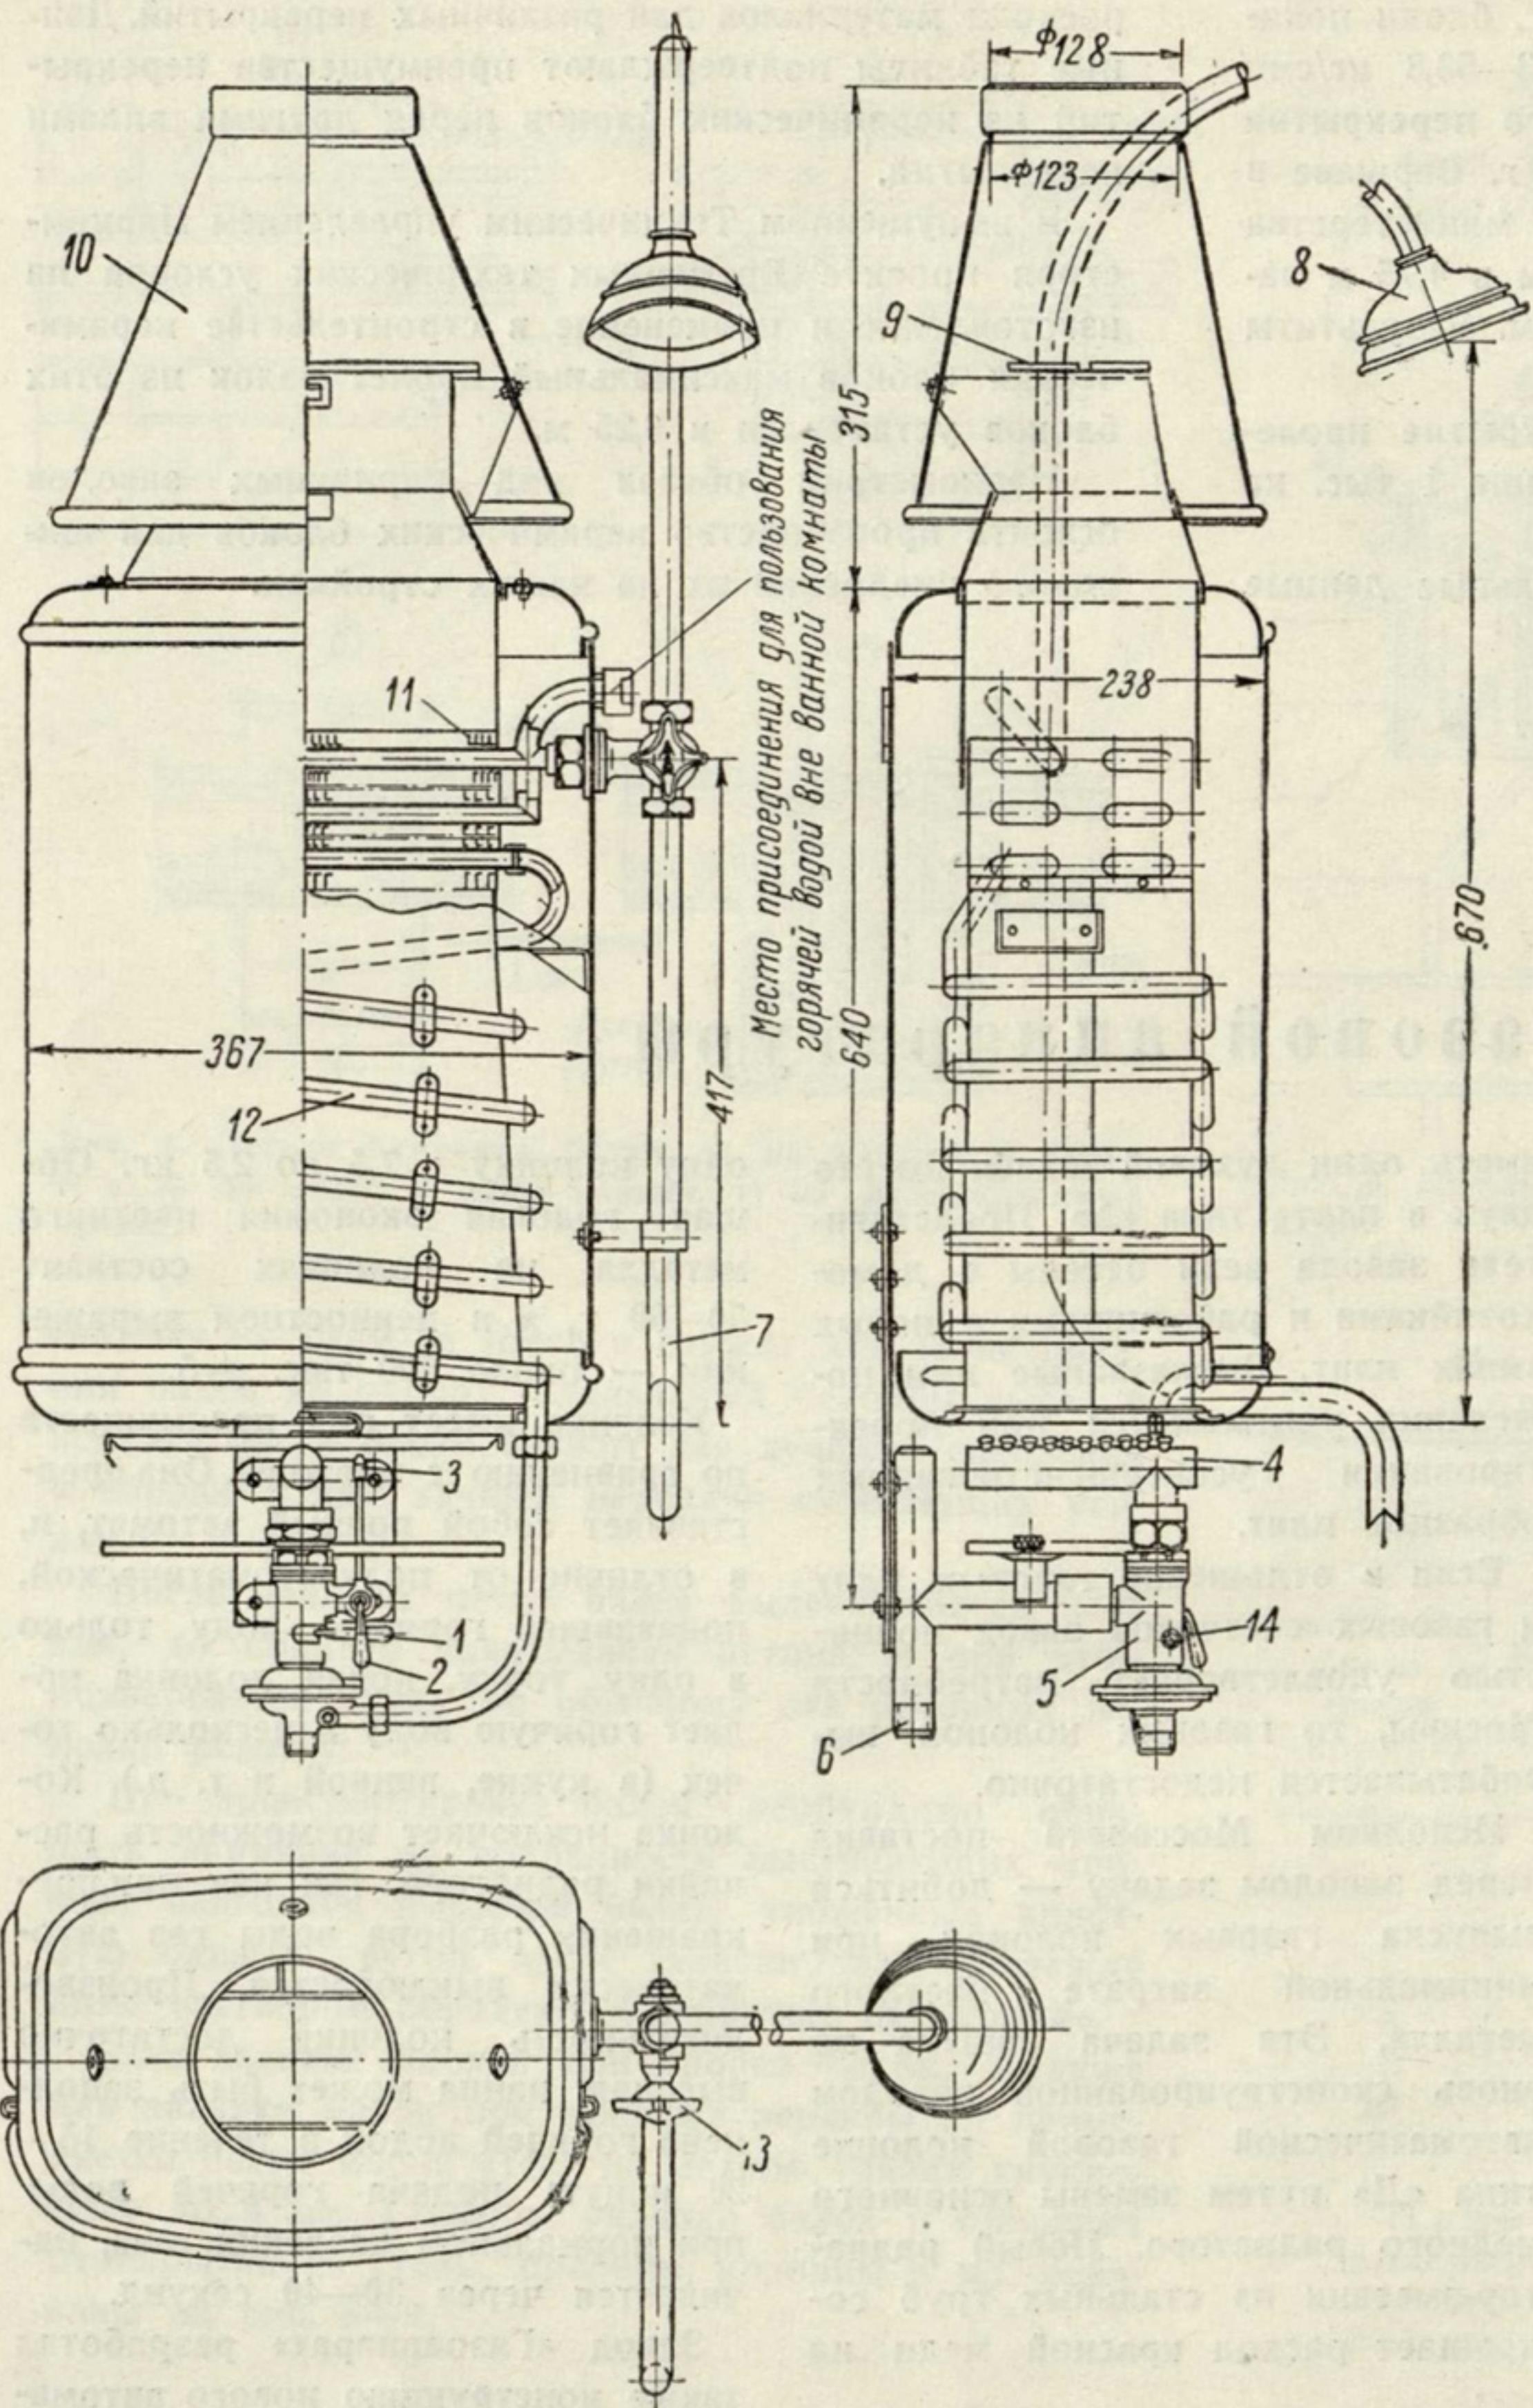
Газовая колонка типа «Д»: 1) ручка газового крана; 2) ручка запальника; 3) защельник; 4) горелка; 5) блок-кран; 6) подводка газа; 7) сливная труба; 8) душ; 9) прерыватель тяги; 10) колпак с прерывателем тяги; 11) пластины теплообменника; 12) змеевик радиатора; 13) распределительный кран; 14) винт для регулирования газа.
